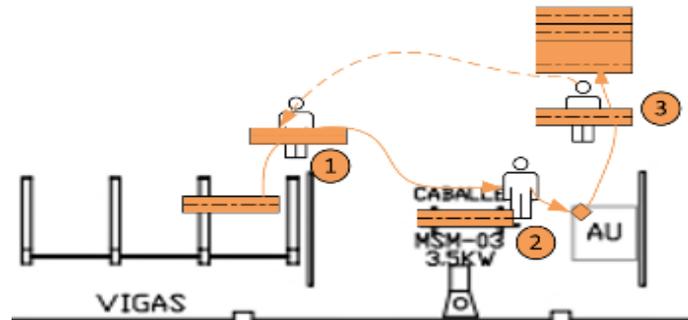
Operación de soldadura plana, apuntalado y reforzado con un operador
